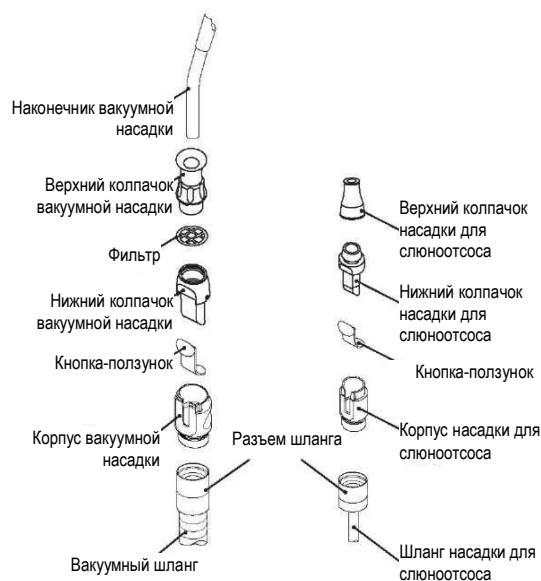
Вакуумная насадка и насадка для слюноотсоса
